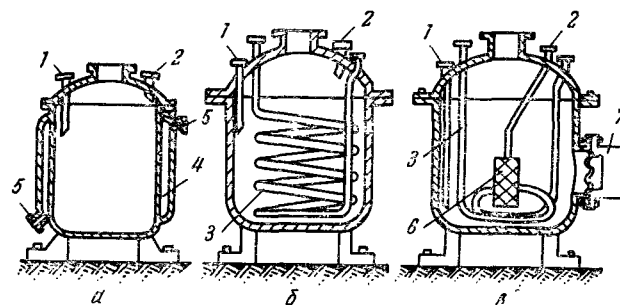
Конструкции испарителей пентакарбонила железа: а — с наружной рубашкой; б — с внутренним змеевиком; в — с барботером, через который подается окись углерода; 1 — ввод карбонила; 2 — ввод продувочного газа; 3 — обогреваемый змеевик; 4 — обогреваемая рубашка; 5 — штуцер ввода пара и вывода конденсата; 6 — металлокерамический барботер; 7 — уровнемер мембранного типа
